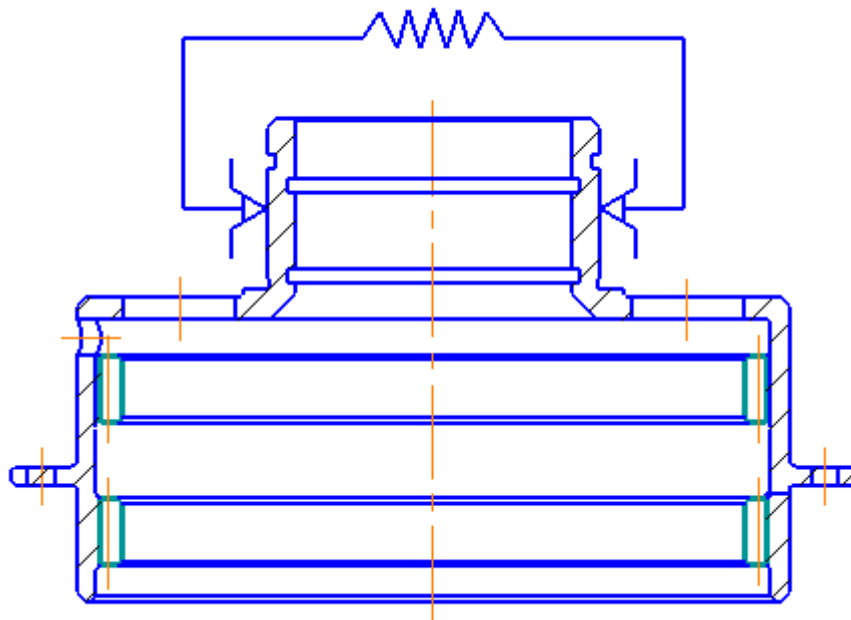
Схема базирования заготовки в схвате промышленного робота
